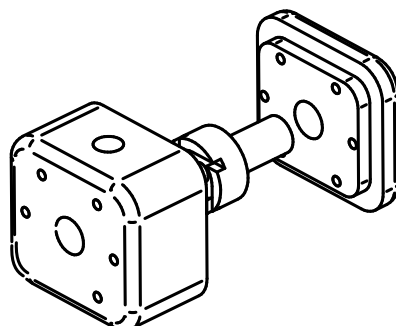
Câmara de Vórtice e Injetor de Ar - Vista Explodida
